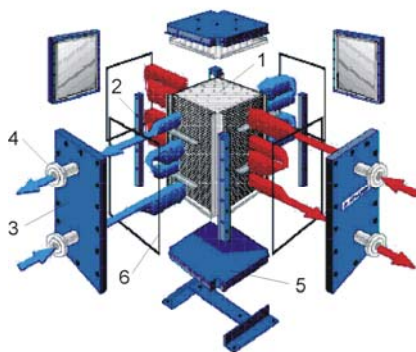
Конструкція теплообмінника КОМПАБЛОК фірми «Альфа Лаваль»: 1 – пакет пластин; 2 – напрямна; 3 – бічна плита; 4 – патрубок; 5 – центральна плита; 6 – ущільнення плити.
